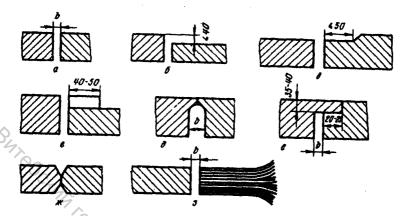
Типы стыковых соединений, полученных электрошлаковой сваркой: а и б – с равными и разными толщинами свариваемых кромок; в – с уменьшением одной кромки до размеров сопрягаемой; в – с увеличением толщины более тонкой кромки; д – с фигурной разделкой кромок; в – «замковое соединение»; ж – Х-образное соединение; з – соединение монолит-
